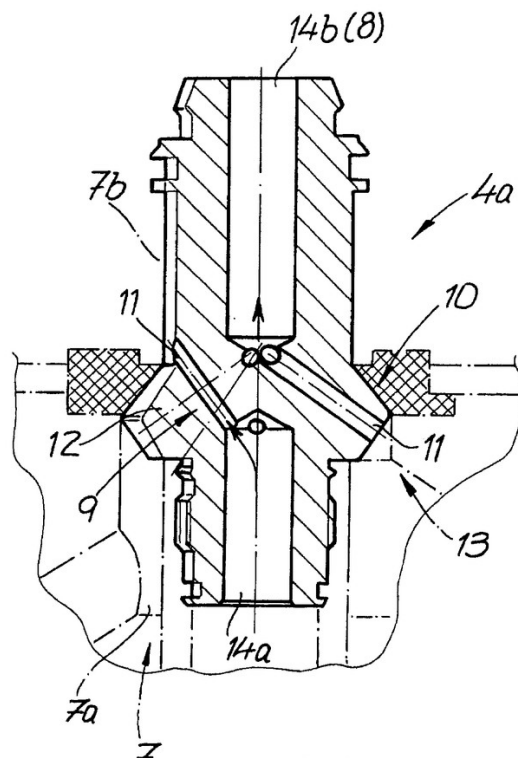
Схема наповнювальної головки-дозатора
